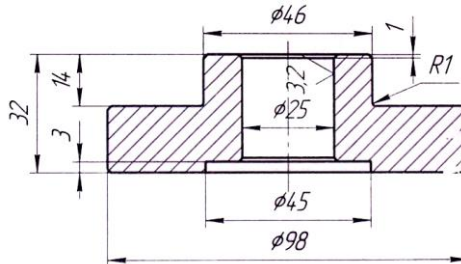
Конструкція і розміри нижньої шайби
